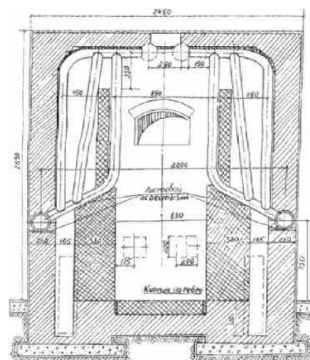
Поперечный разрез котла НР-18 с пакетом из гнутых труб
